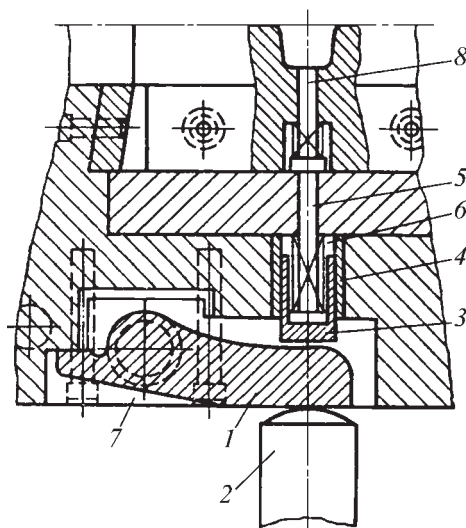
Рычажно-кулачковый выталкивающий механизм:
